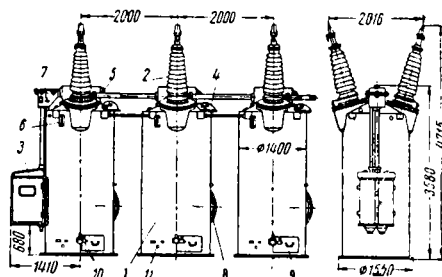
Выключатель типа ВМ-35: 1—шкаф с приводом; 2—ручное отключение; 3—газоотводная труба и аварийный клапан; 4—съемная лебедка для подъема и опускания баков; 5—поддерживающая конструкция; 6—болт заземления; 7—указатель уровня масла; 8—масловыпускной вентиль; 9—шарнирная муфта; 10—кабельная муфта
